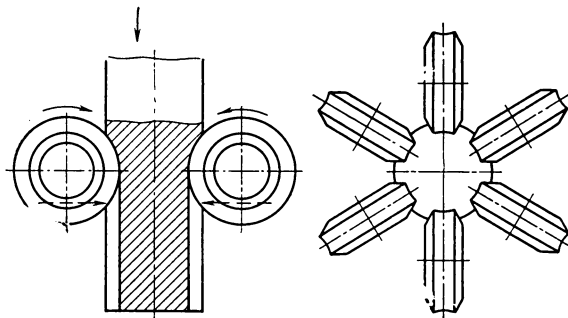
Схема продольного накатывания зубьев вала многороликовой головкой
